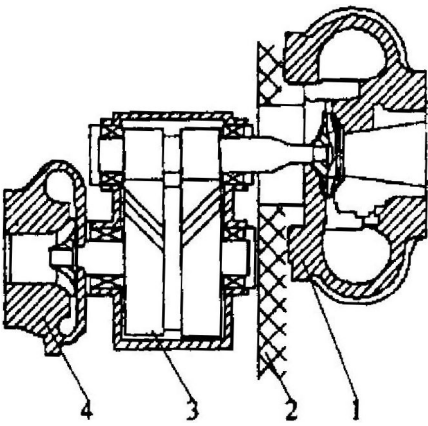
Редукторний двухвальний ДКА з розміщенням ДС в блоці розділення повітря: 1 - детандерна ступінь; 2 - теплоізоляція з перліту; 3 - турборедуктор; 4- компресорна ступінь
